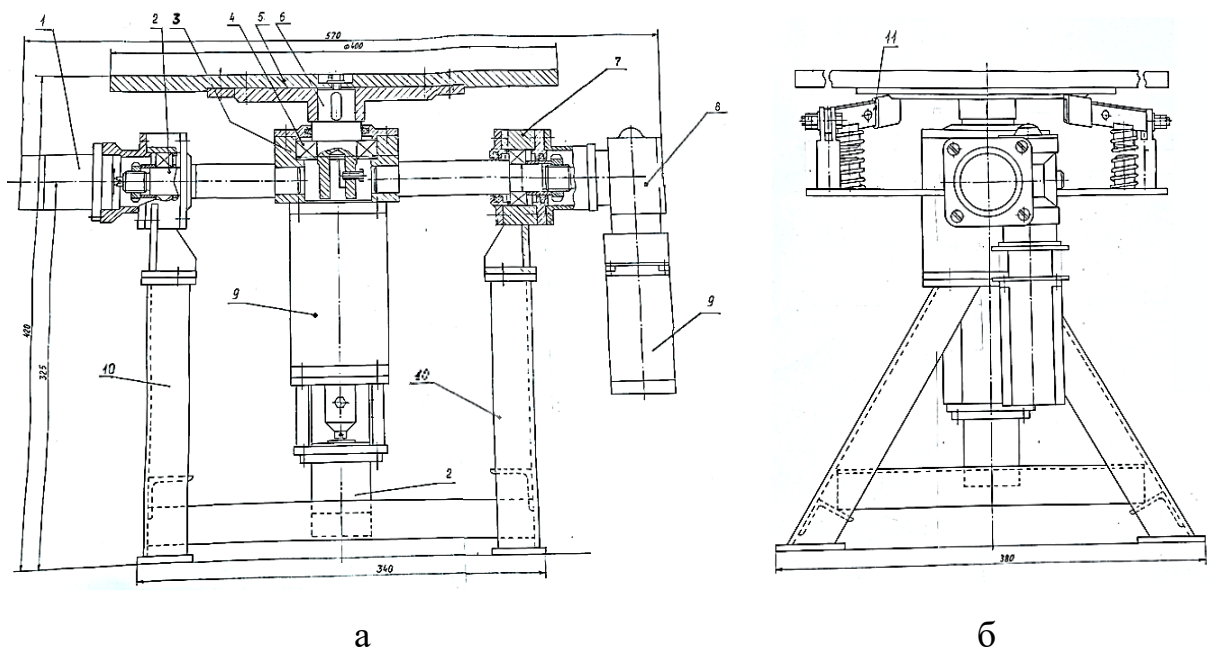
Загальний вигляд УЗО установки наплавлення:
